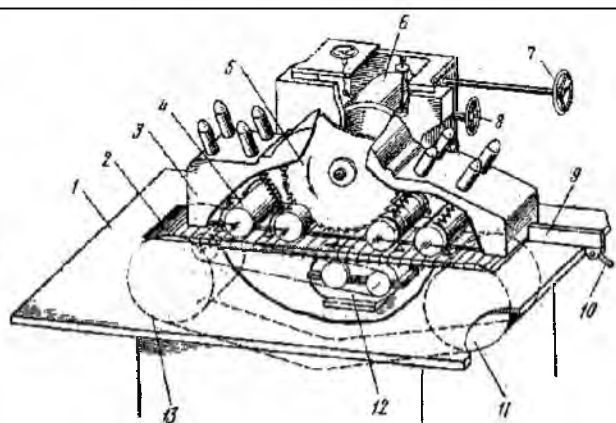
Гидрокинематическая схема одностороннего рамного ши-порезного станка ШО-16-4
